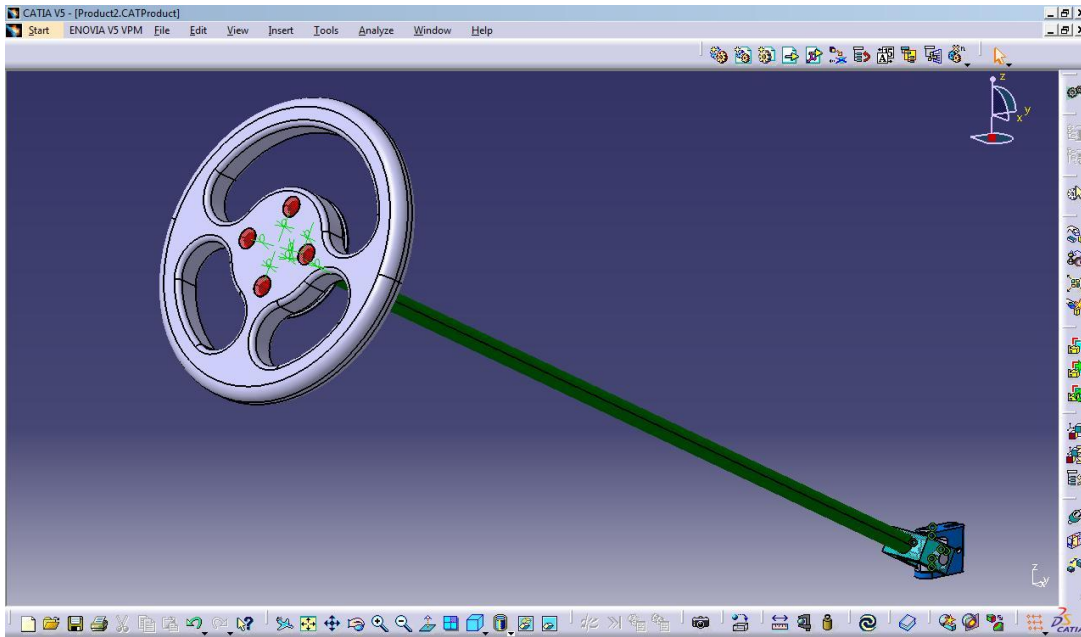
Explosión del Sub-ensamble del eje de dirección
